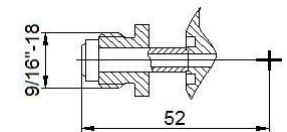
Штуцер (входной) для торцевого уплотнения Ni шайбой с втулкой с дюймовой резьбой 9/16"-18
